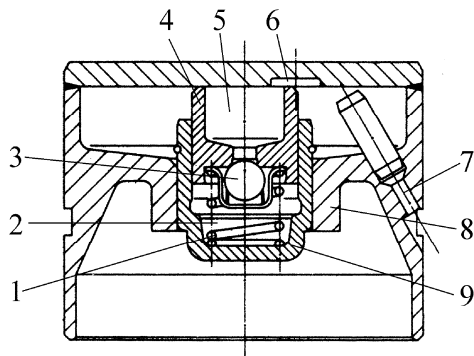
Гидрокомпенсатор теплового зазора: 1 – пружина; 2 – рабочая полость высокого давления; 3 – обратный клапан; 4 – поршень; 5 – масляная полость; 6 – перепускная канавка; 7 – масляный канал; 8 – корпус; 9 – цилиндр
